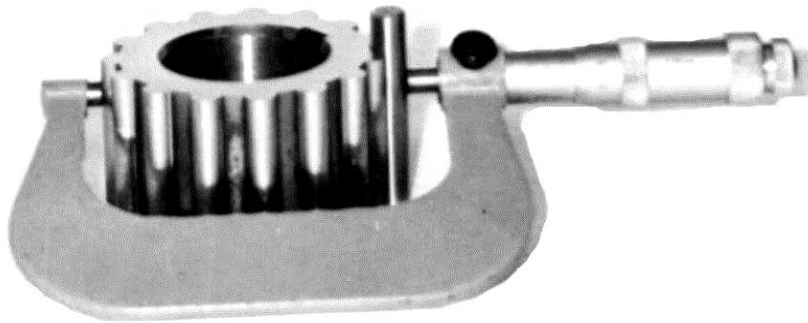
Измерение погрешности формы зубчатого контура шестерни (параметр $1б$)
